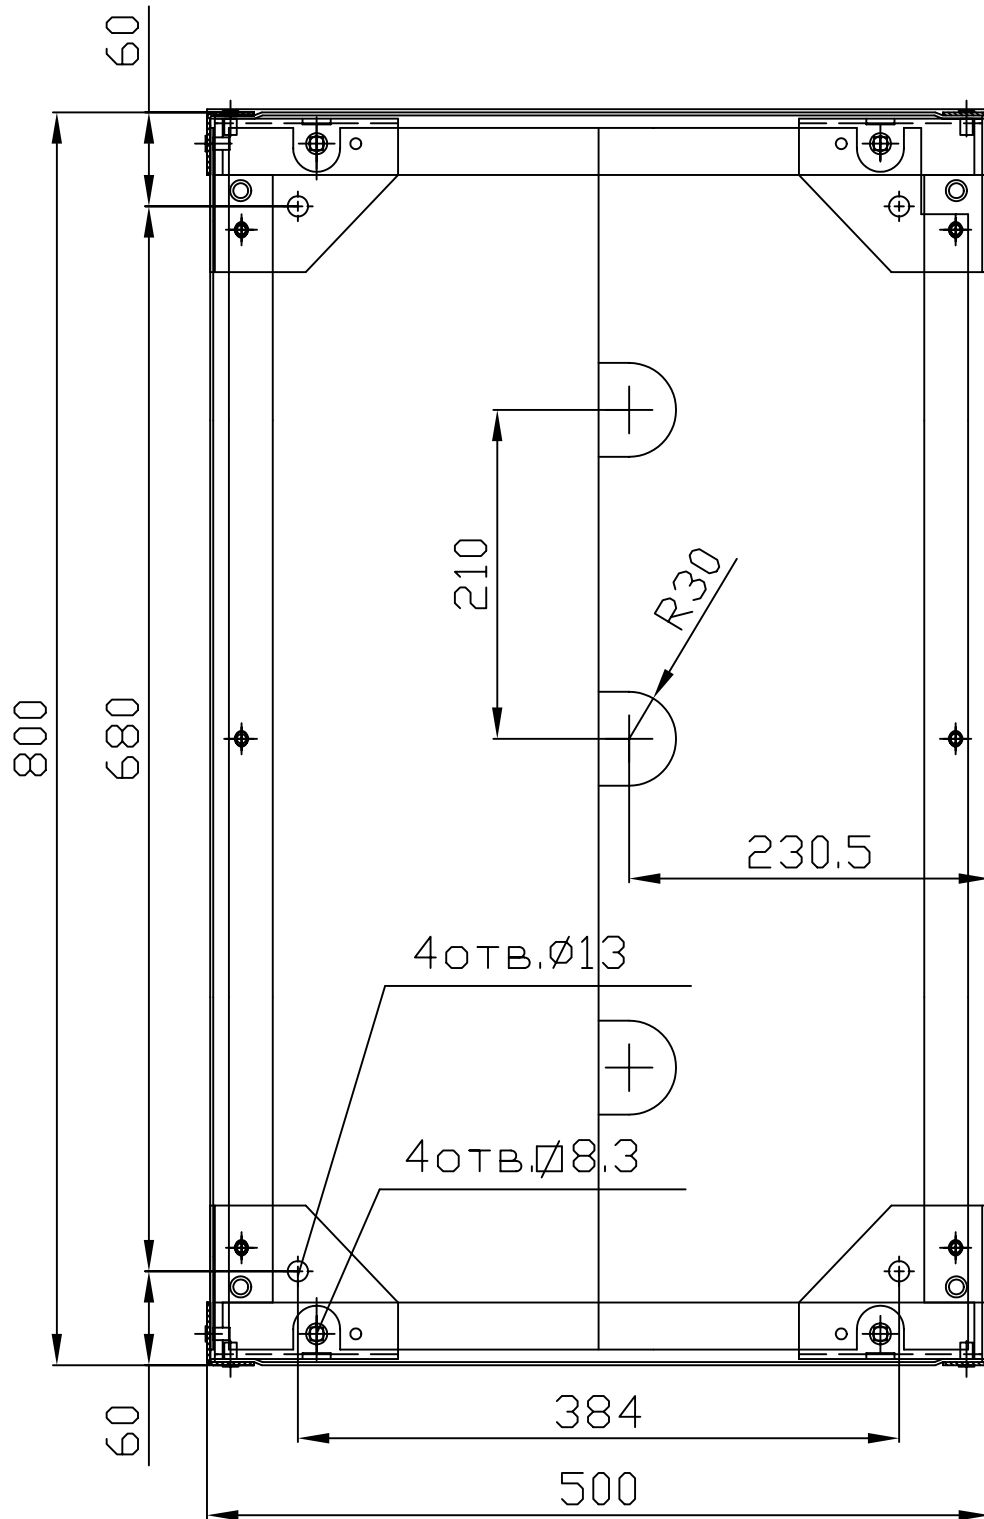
Установочные размеры камеры КСО шириной 500 мм.
